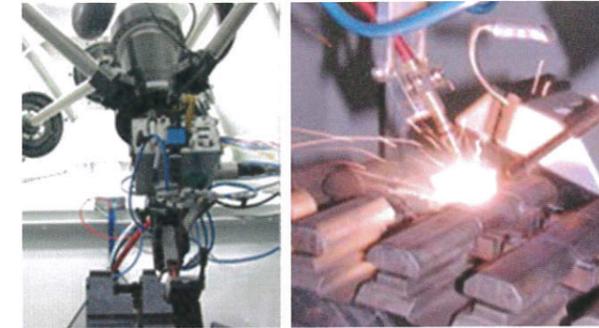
maschinelle Laserschweißeinrichtung zur Stegverbindung
